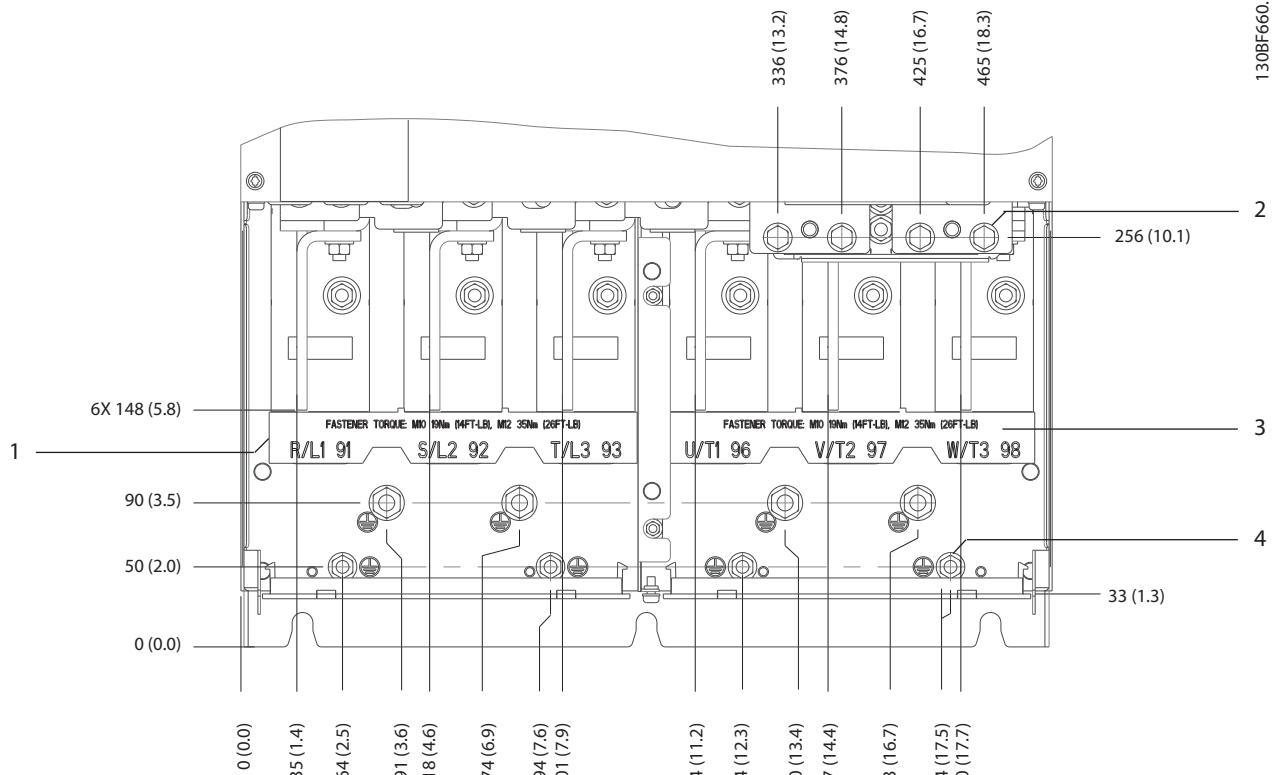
Dimensi Terminal E2h (Tampak Samping)
